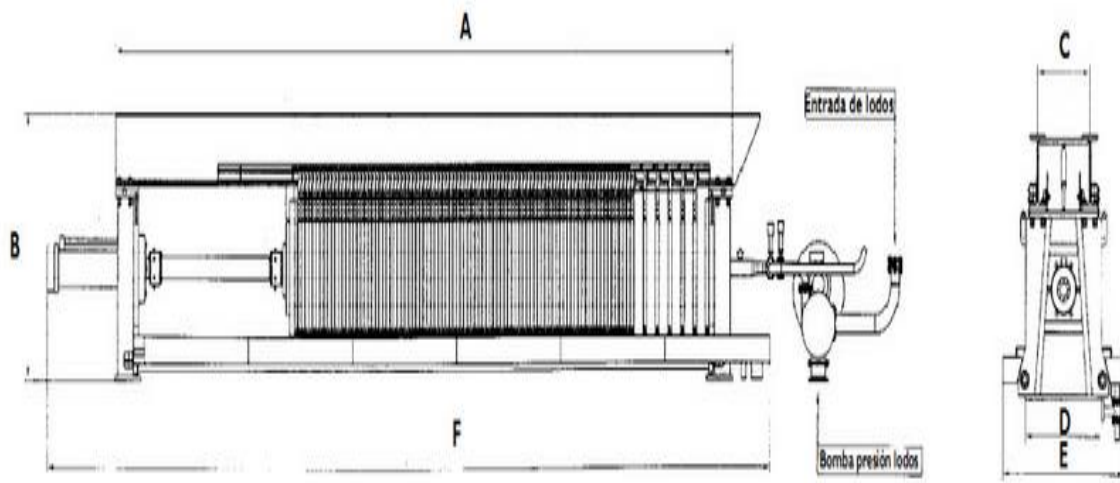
Imagen que muestra alzado y perfil de filtro prensa
